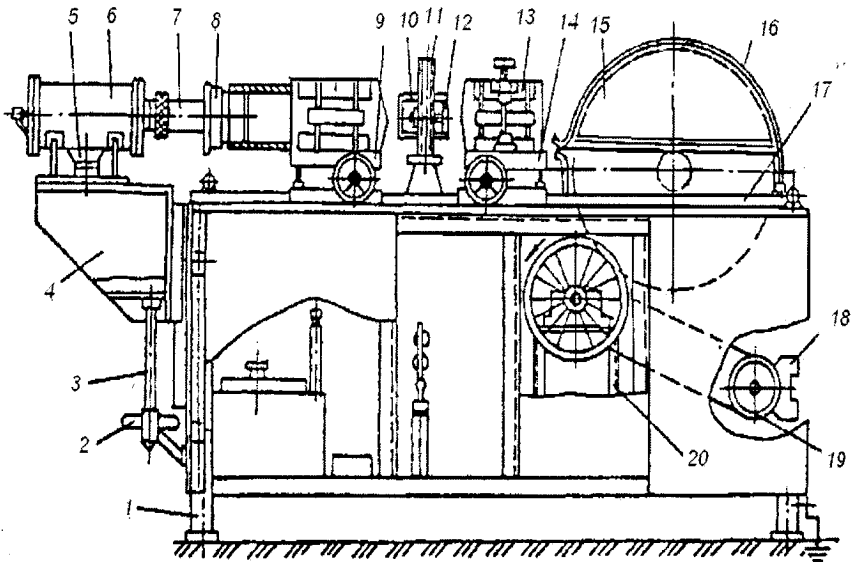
Універсальний верстат для оброблення й зварювання пластмасових труб: 1 — станина; 2 — гайка; 3 — гвинт; 4 — кронштейн; 5 — чотириходовий кран; 6 — пневмоциліндр; 7 — шток; 8 — формувальний дорн; 9, 14 — супорти; 10 — гільза; 11 — електричний нагрівач; 12 — змінний дорн; 13 — поворотні затискачі; 15 — дискова пила; 16 — шарнірний кожух; 17 — напрямна; 18 — електродвигун; 19 — клиновий пас фрези; 20 — фреза
